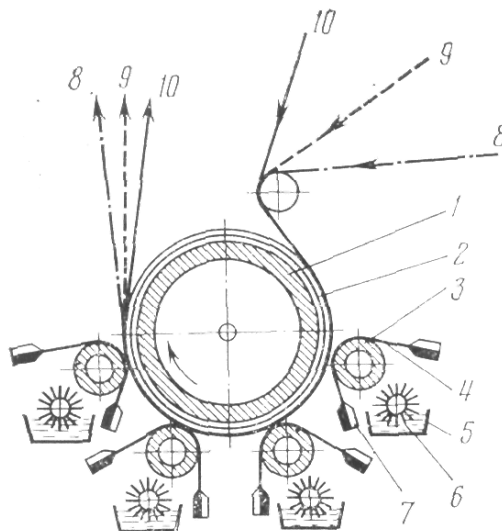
Схема цилиндрической печатной машины с гравированными валами
